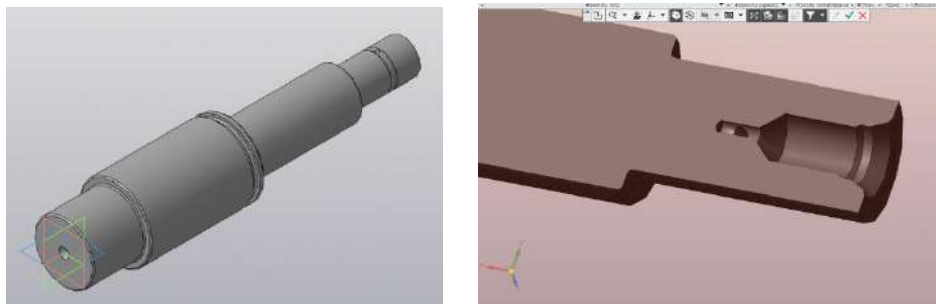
3D-модель детали «Вал» и ее разрез в месте расположения ступенчатого отверстия
